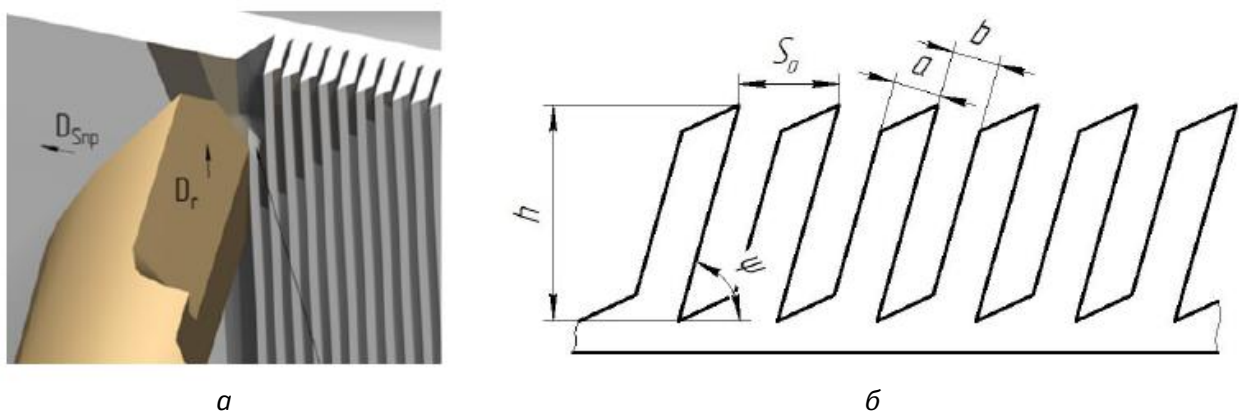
а* — схема получения оребрения методом деформирующего резания: 1 — резец; 2 — обрабатываемый материал; 3 — полученное оребрение; *б* — профиль получаемого оребрения: h — высота структуры; S_0 — шаг ребер; φ — угол наклона ребра; a — ширина ребра; b — ширина межреберного зазора
